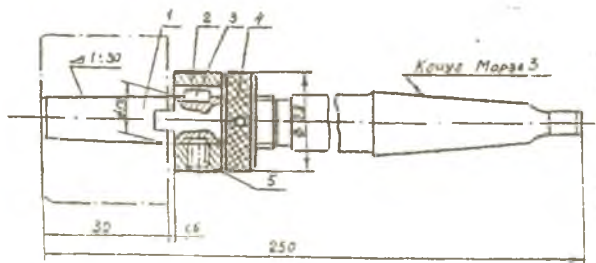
Оправка: 1 - корпус, 2 - поводок, 3 - шпонка
